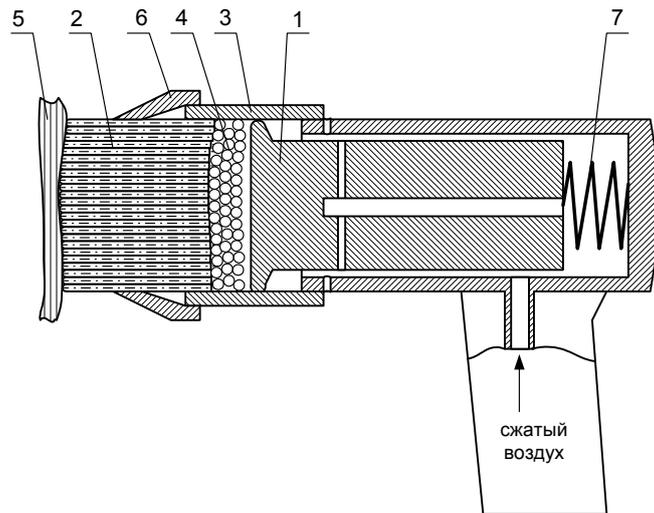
Схема многоконтактного виброударного инструмента ШСУ: 1 — силовой привод, 2 — пакет круглых стержней, 3 — корпус упрочнителя, 4 — стальные шары, 5 — обрабатываемая деталь, 6 — цанговый зажим, 7 — упругий элемент
